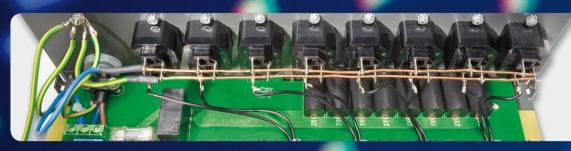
Die komplett verkabelten Kaltgerätebuchsen.
